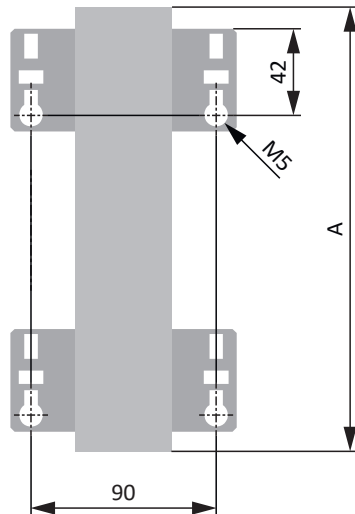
Bohrplan PMC KWADQU mit MWS 310L
